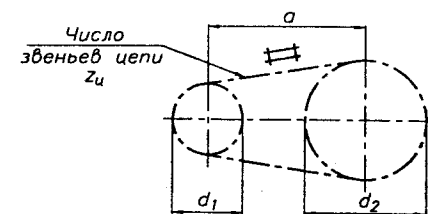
Схема и основные размеры передачи с приводной роликовой (втулочной) цепью
